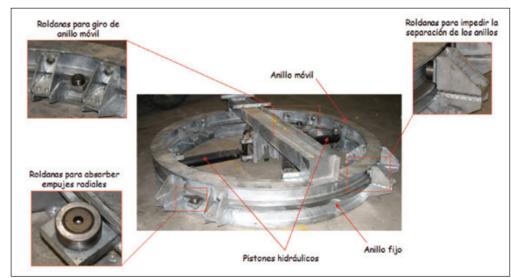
Detalle de los elementos que componen el sistema de giro en el plano acimutal.
